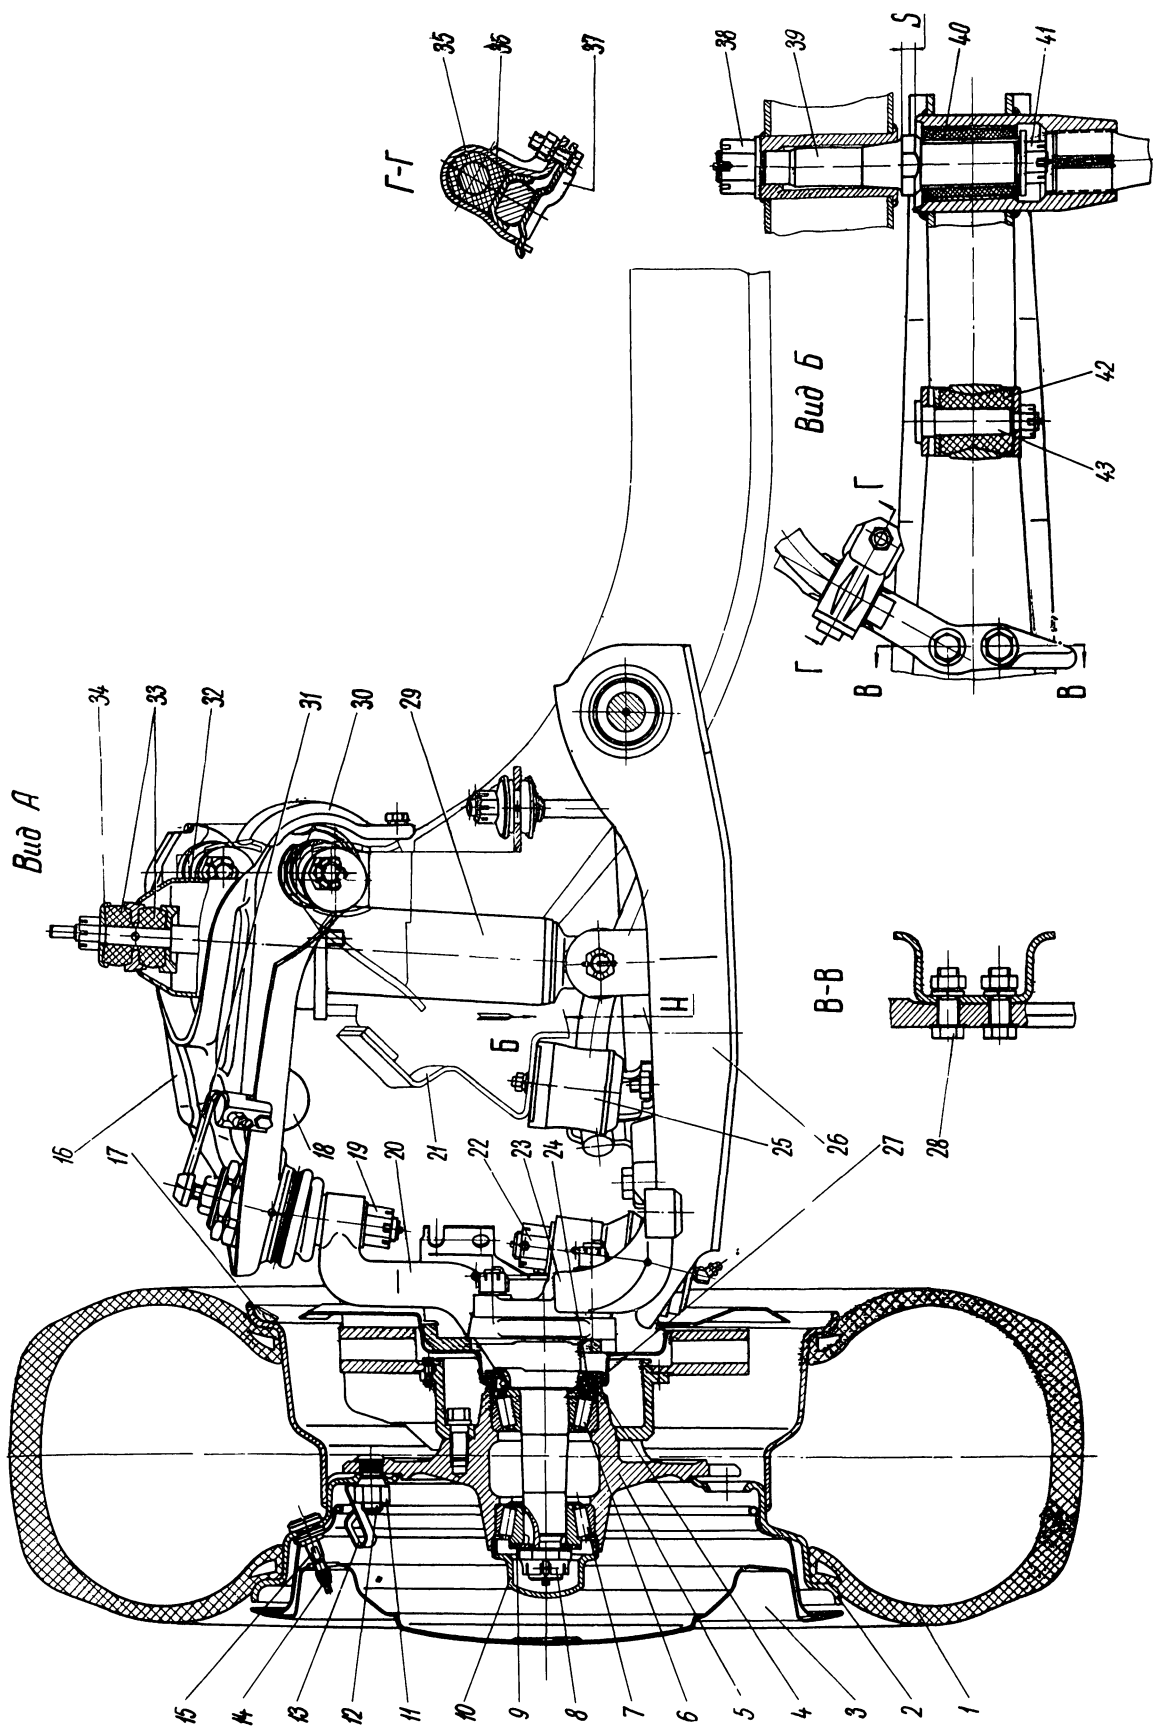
Передняя подвеска с колесами в сборе ( вид сверху )
